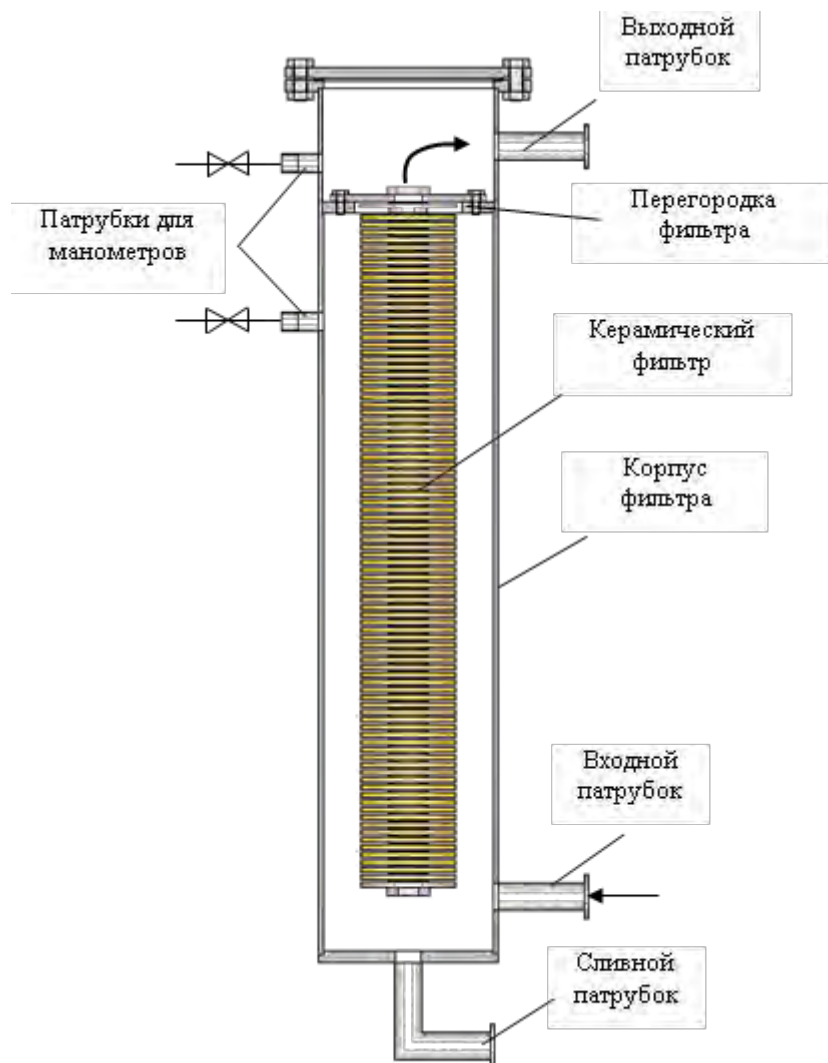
Конструкция полупромышленного образца керамической фильтрующей установки
